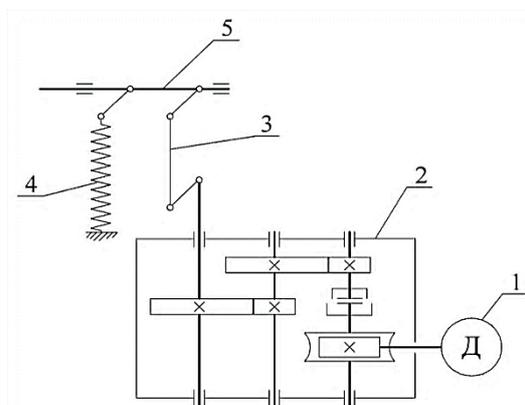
Кинематическая схема шлагбаума AN MOTORS ASB6000
